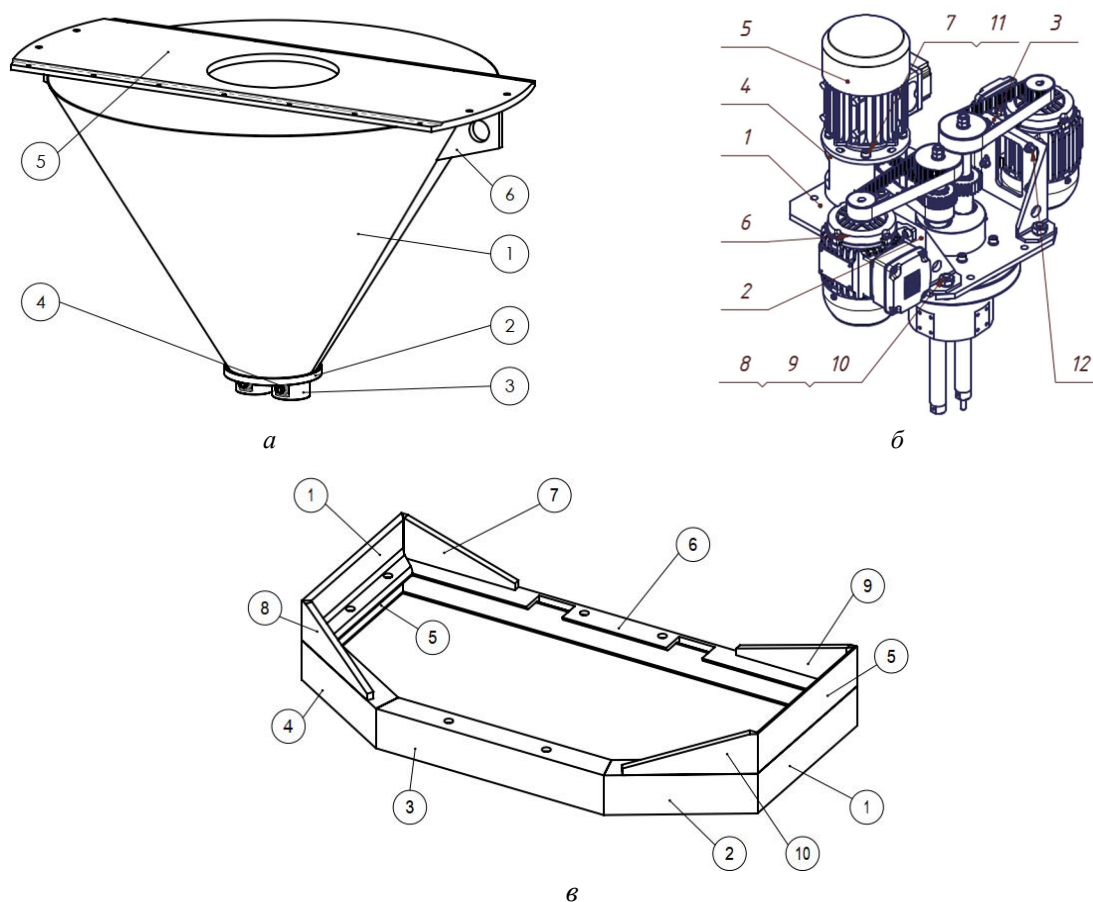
Основні вузли дозатора: а – конічний бункер; б – механічний привод; в – рама
